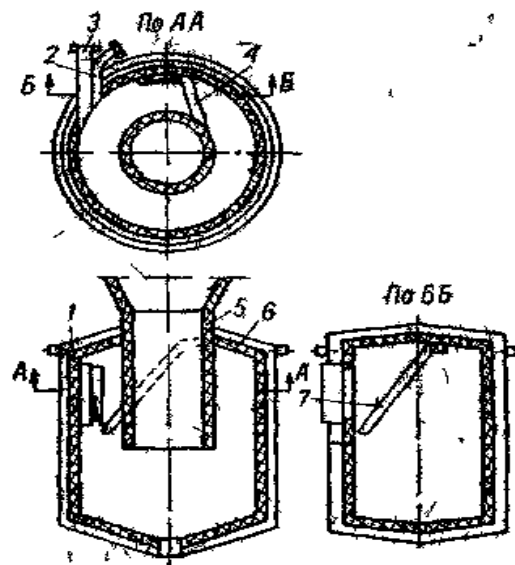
Принципова конструкція циклонної печі з тангенціальним введенням повітря і твердого пестициду: 1 – циліндричний корпус; 2 – горілка; 3 – сопло повітряного дугтя; 4 – виступ внутрішній; 5 – відводний патрубок; 6 – кришка; 7 – виступ
